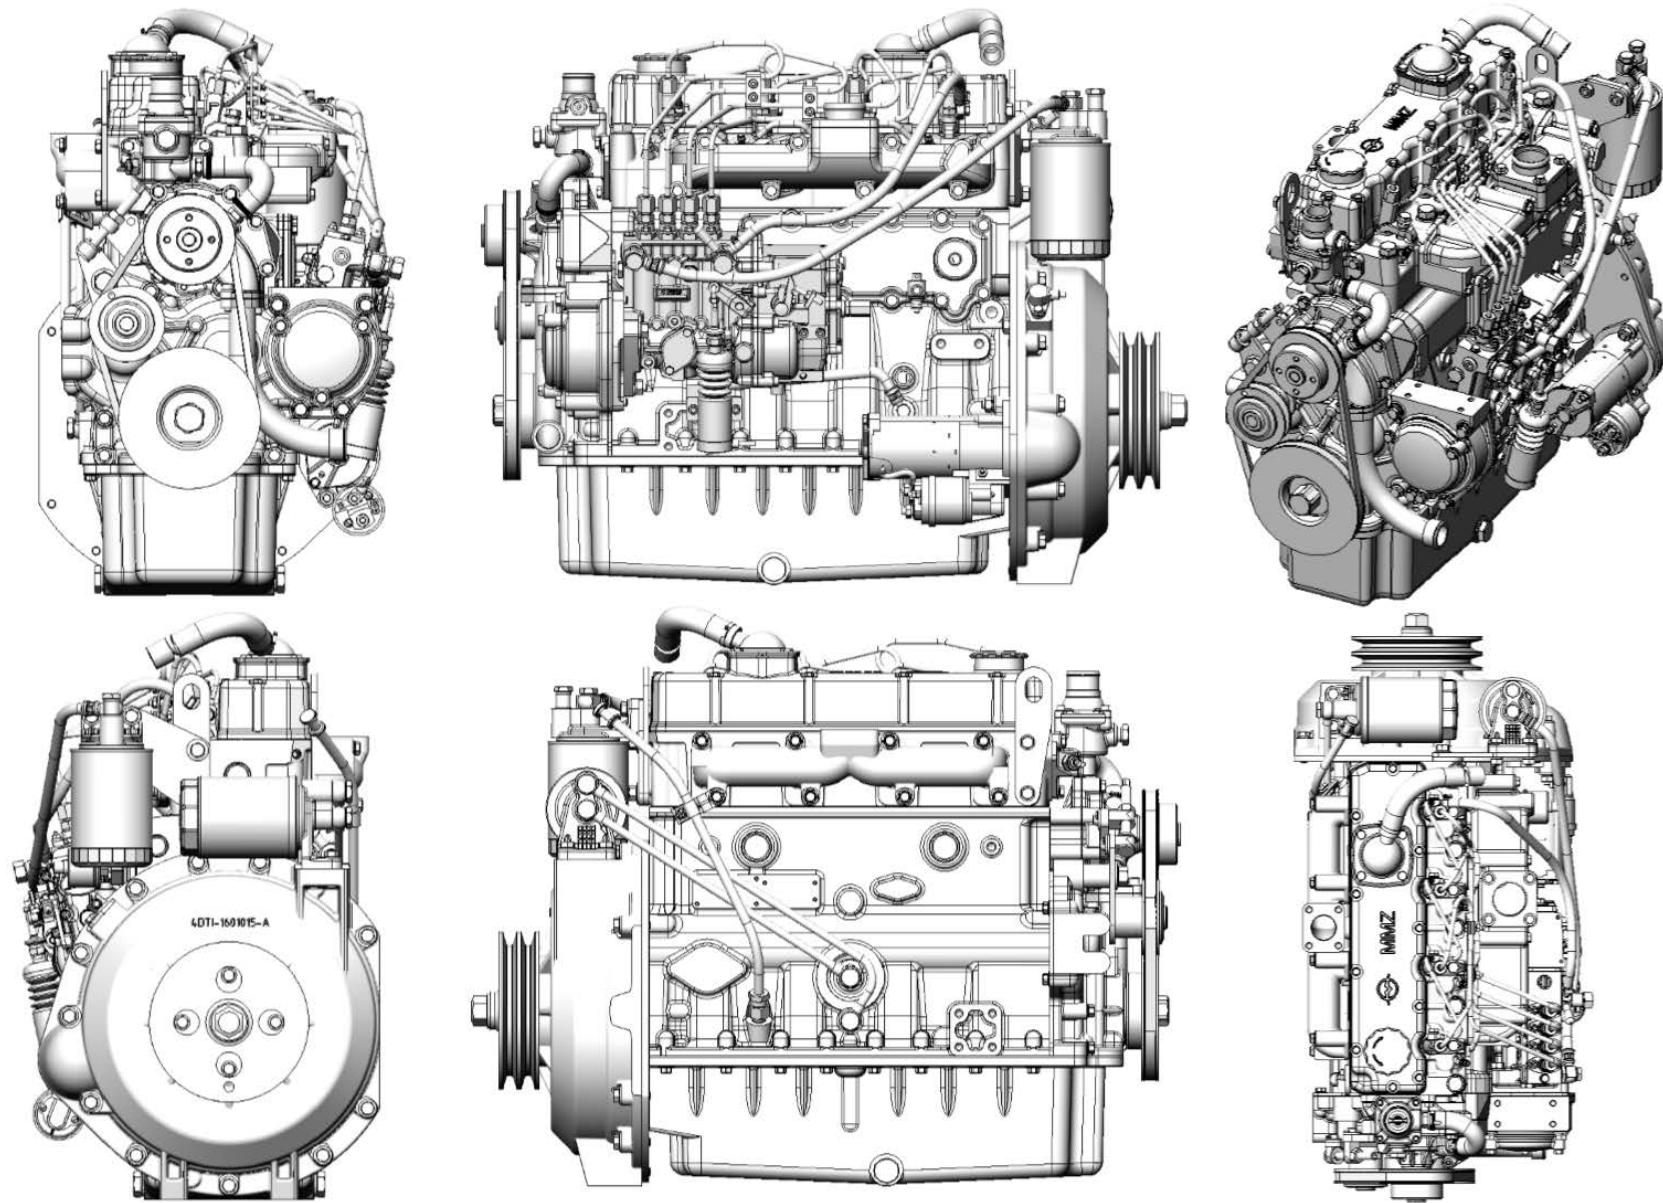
а – Общий вид двигателя MMZ-4DG.1-01
